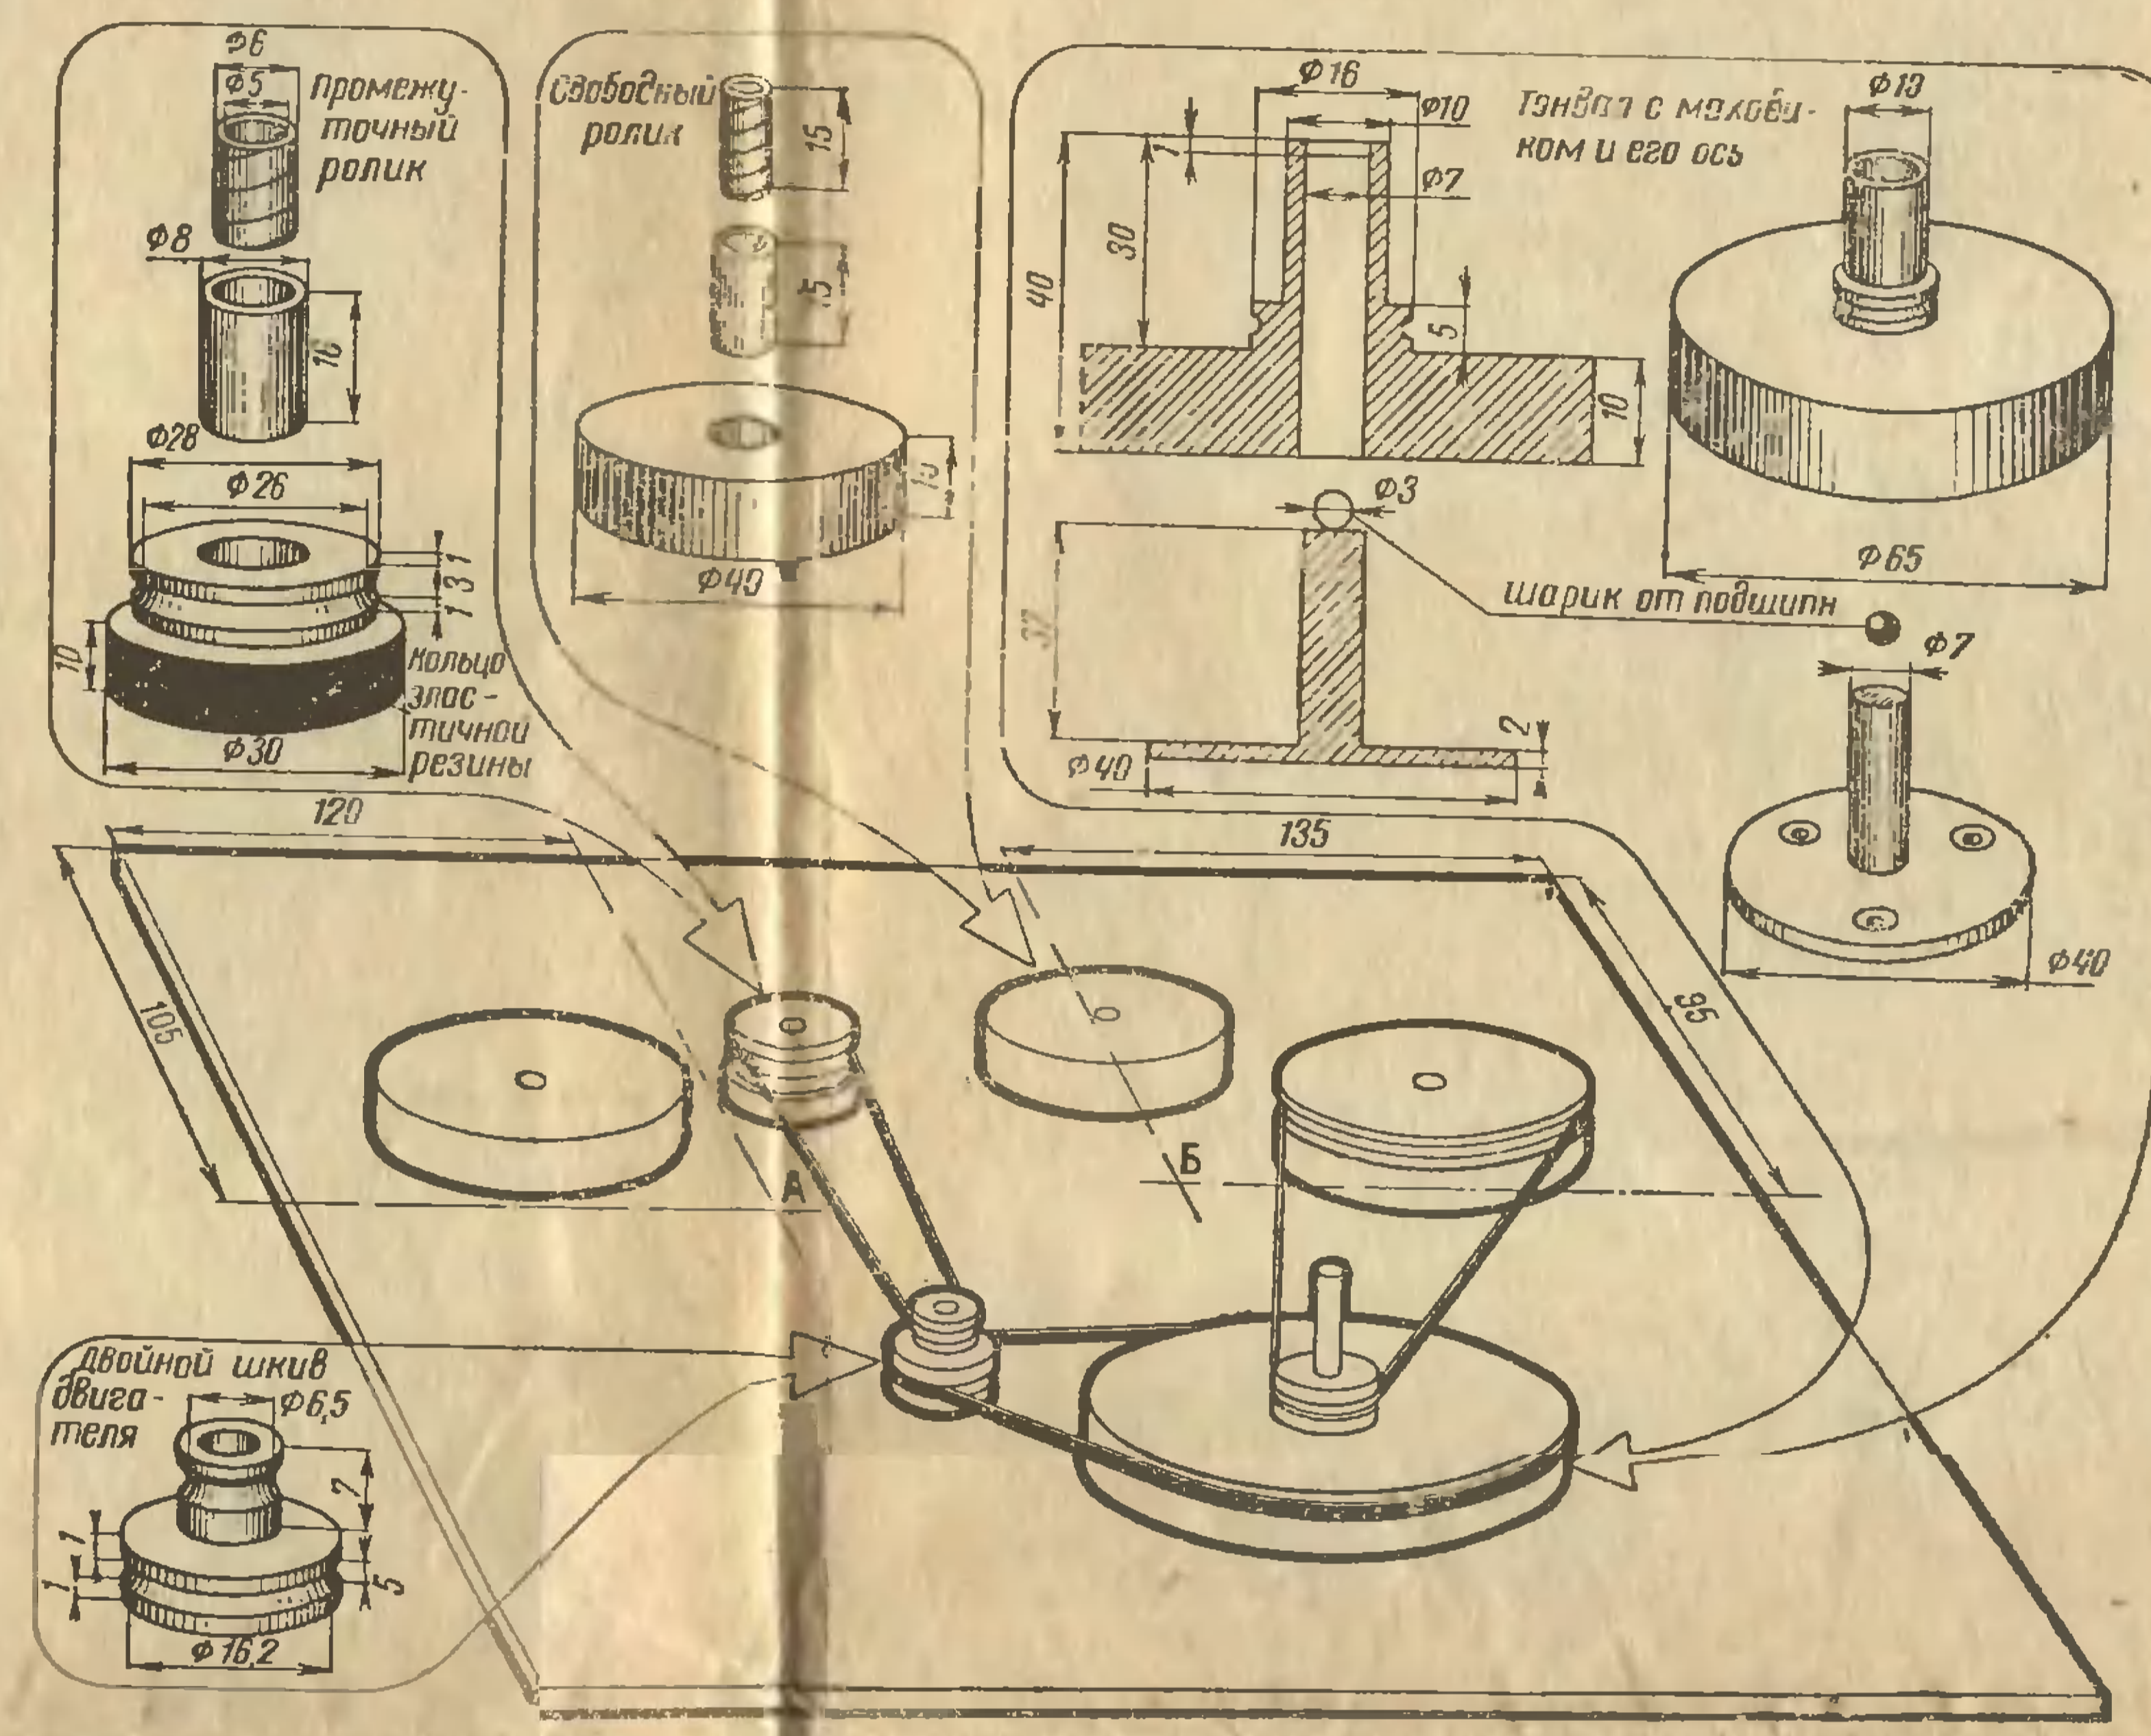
Детали ведущего узла лентопротяжного механизма: А — центр оси рычага подающего узла; Б — центр оси рычага приемного узла
